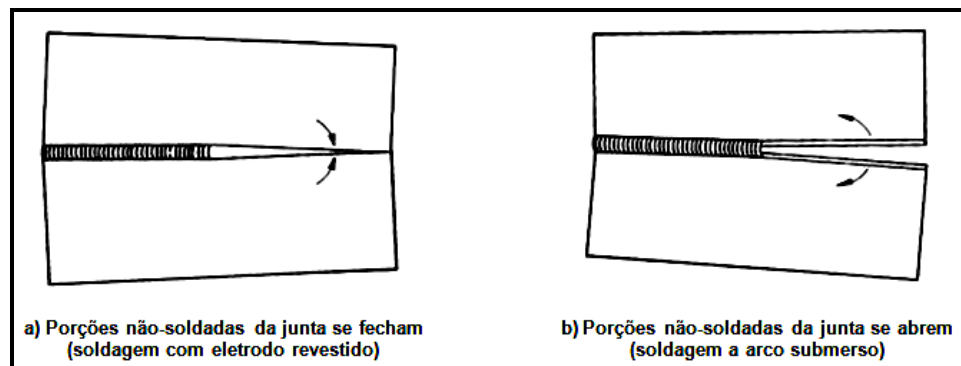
Variação dimensional rotacional em uma junta de topo: (a) soldagem com eletrodo revestido; e (b) soldagem a arco submerso (Adaptado de AWS, 2001).
